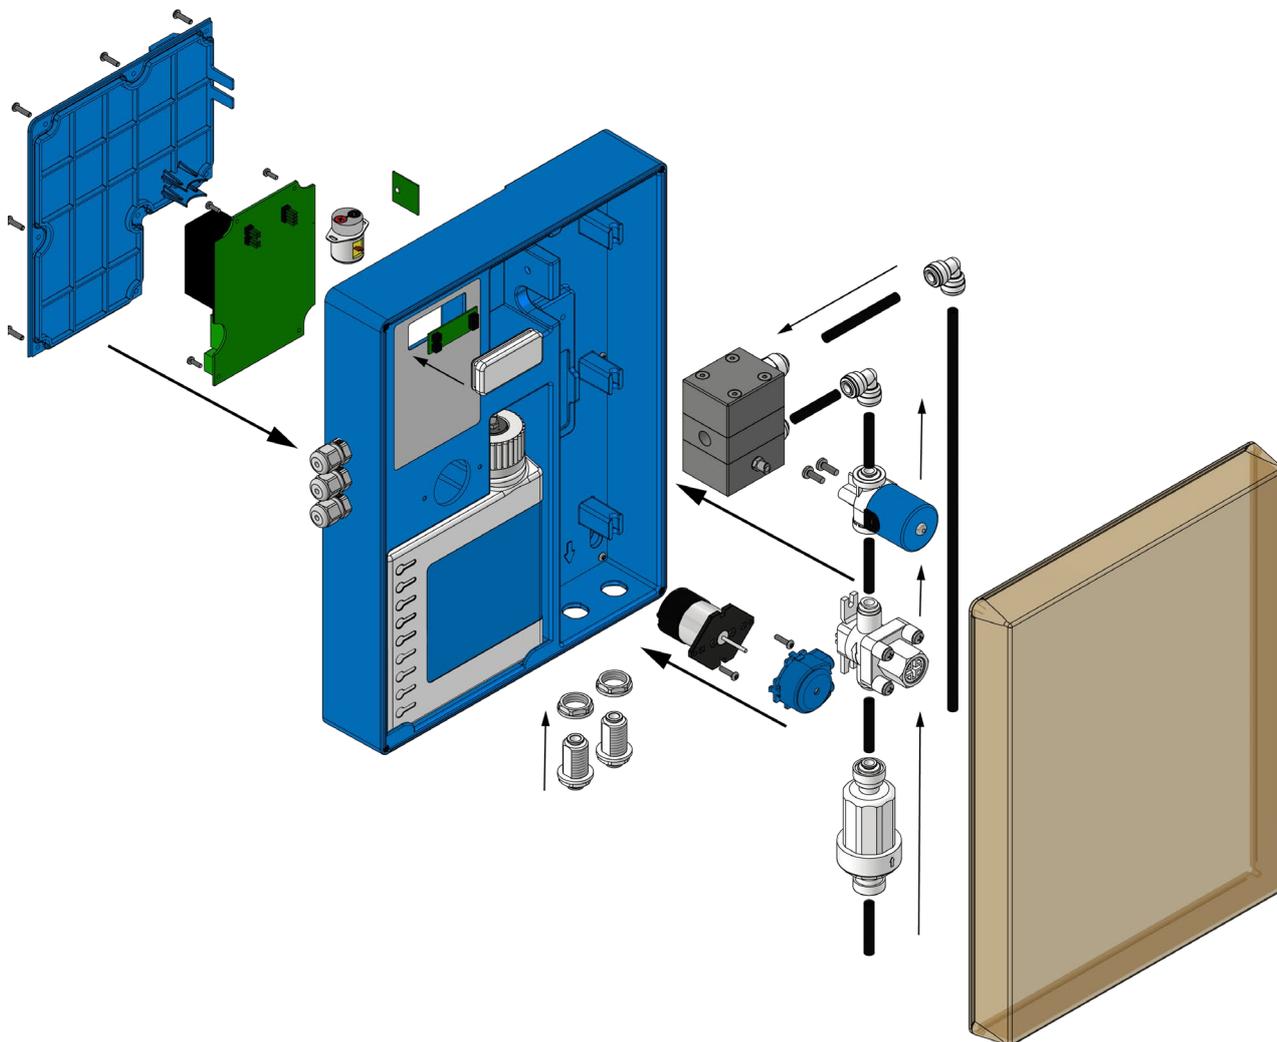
LIMES Explosionszeichnung - Zusammenbau der Komponenten
